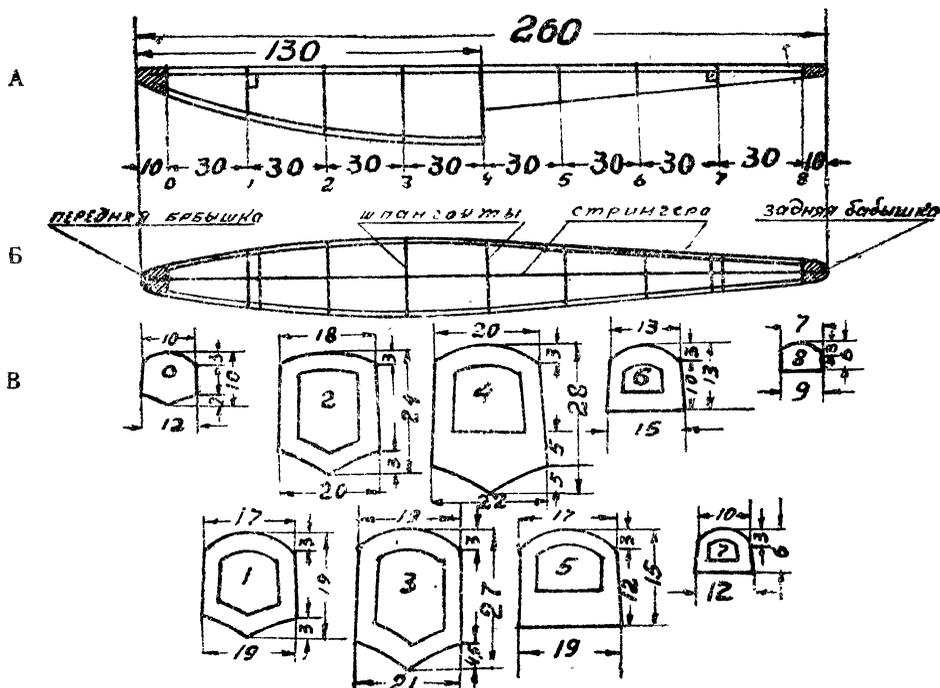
Передние поплавки. А—вид сбоку. Б—вид сверху. В—чертеж шпангоутов.
